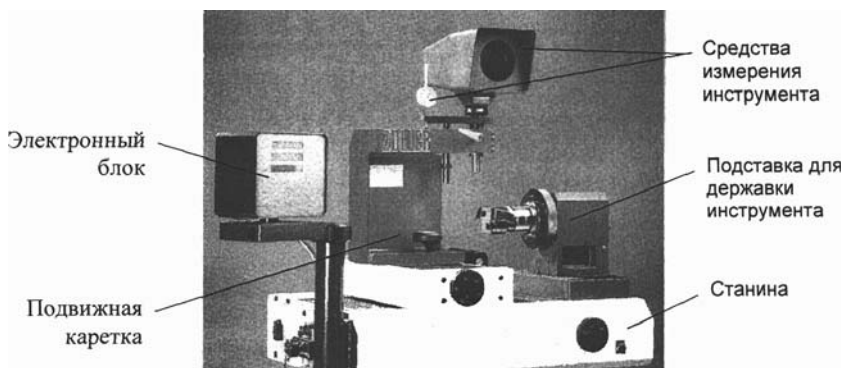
Измерительное приспособление для настройки инструмента вне станка
